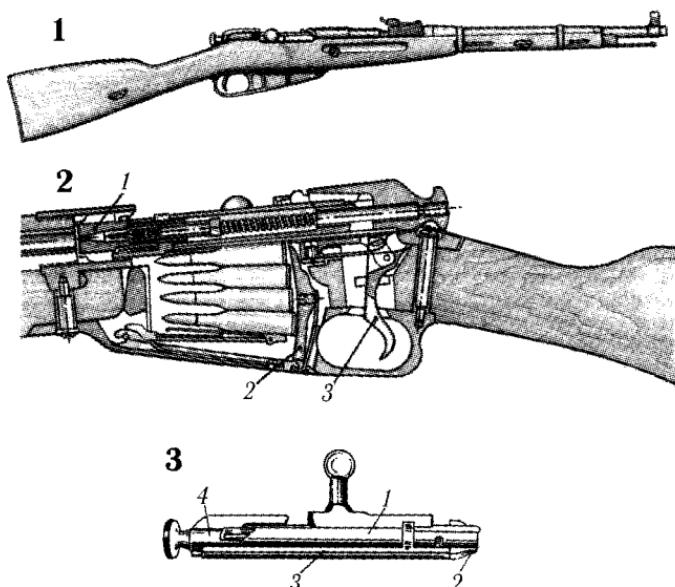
Охотничий карабин КО-44: 1 – общий вид, 2 – разрез затвора, магазинной коробки и спускового механизма, 3 – затвор: 1 - стебель; 2 - боевая личинка; 3 - соединительная планка; 4 - курок.
